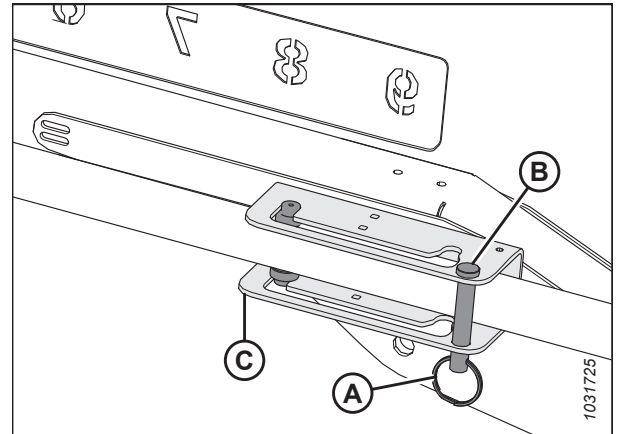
Cilindrul brațului exterior stâng – poziția înainte
